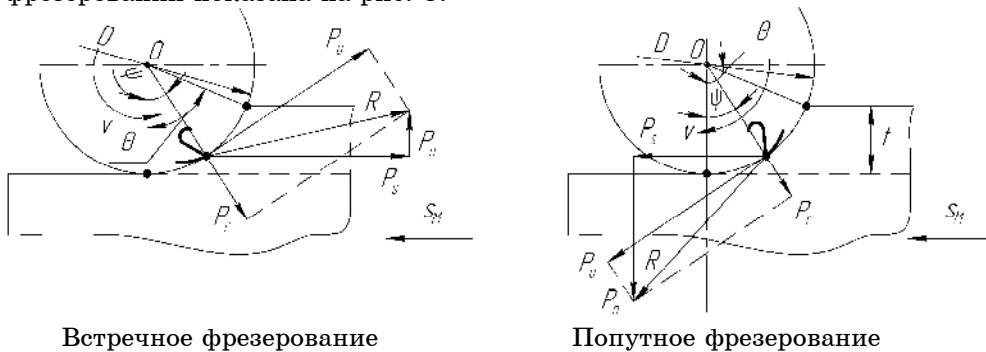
Схема сил, действующих при работе цилиндрической фрезы [10]
